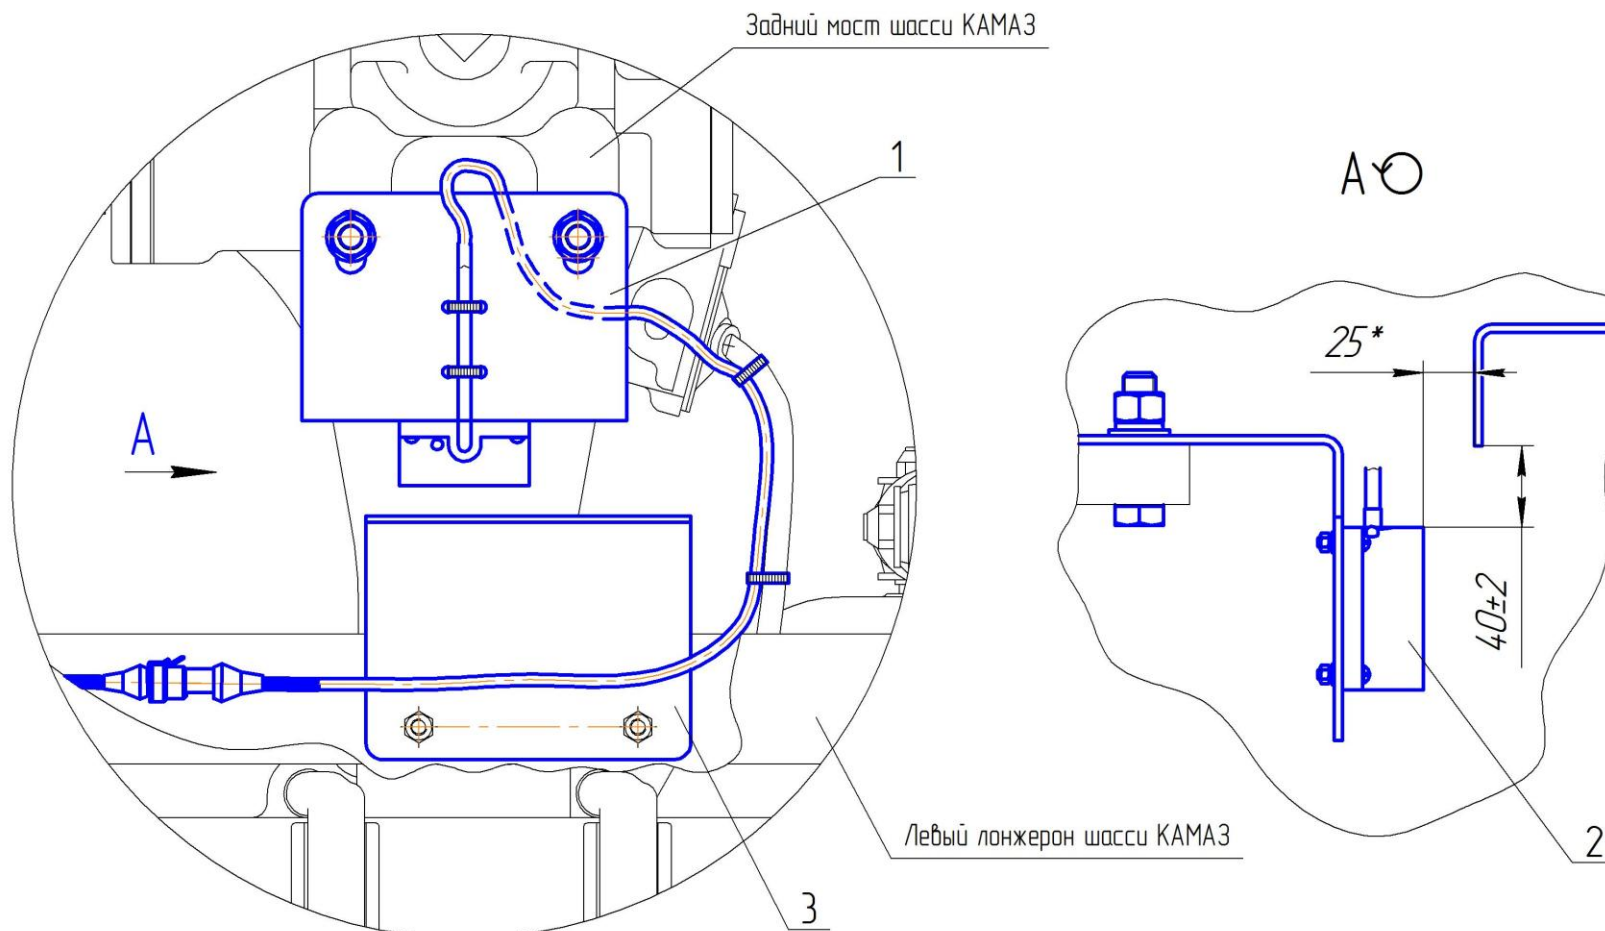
Установка датчика контроля загрузки на мусоровоз КО-456-20 на шасси КАМАЗ
